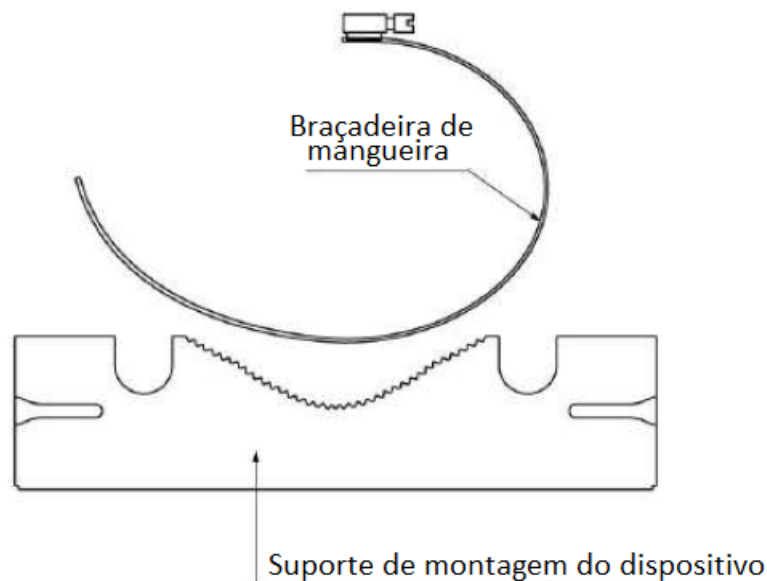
esquema do suporte de montagem do dispositivo e braçadeiras
